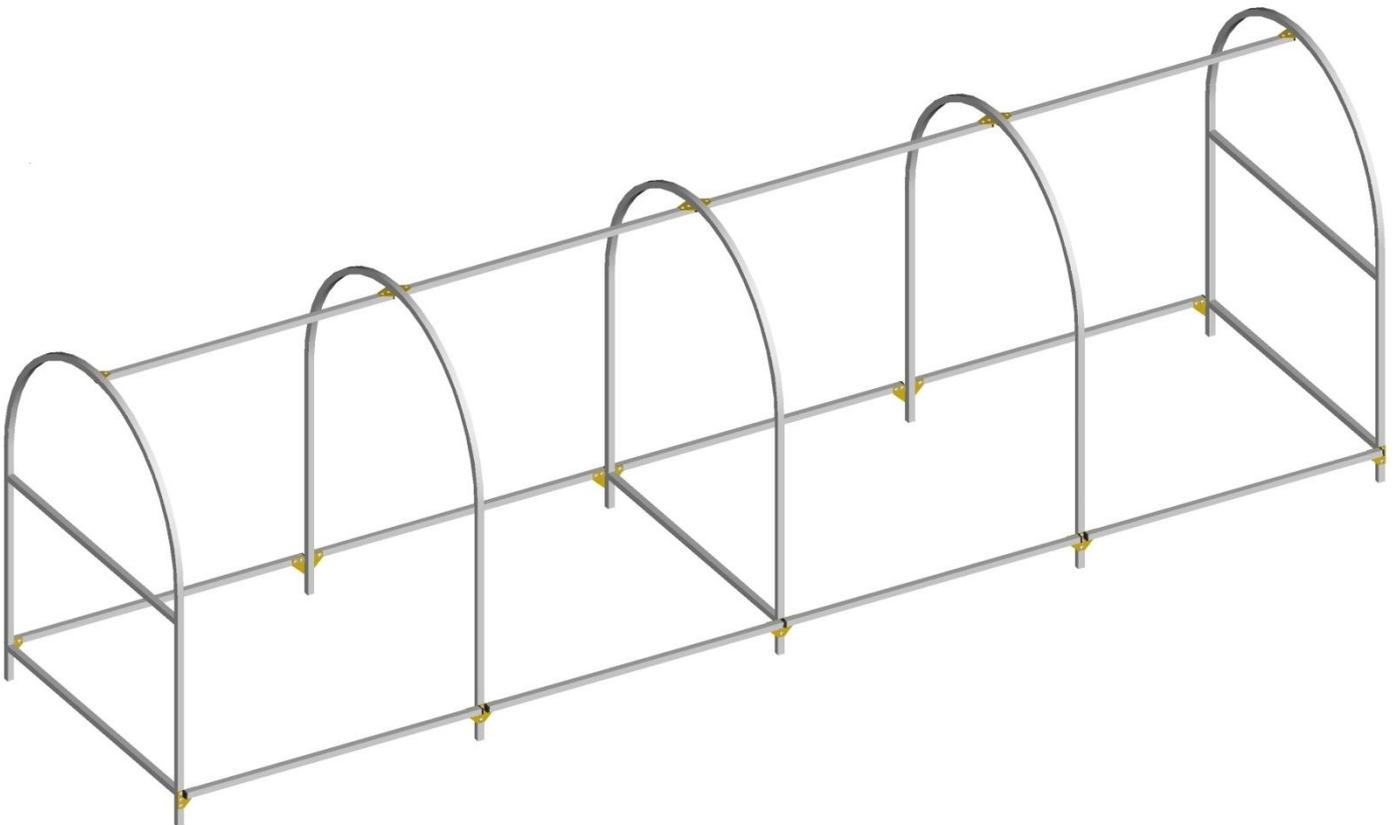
Сборка каркаса для мини-парника размером 4x1 м (базовый и доборный комплекты).
